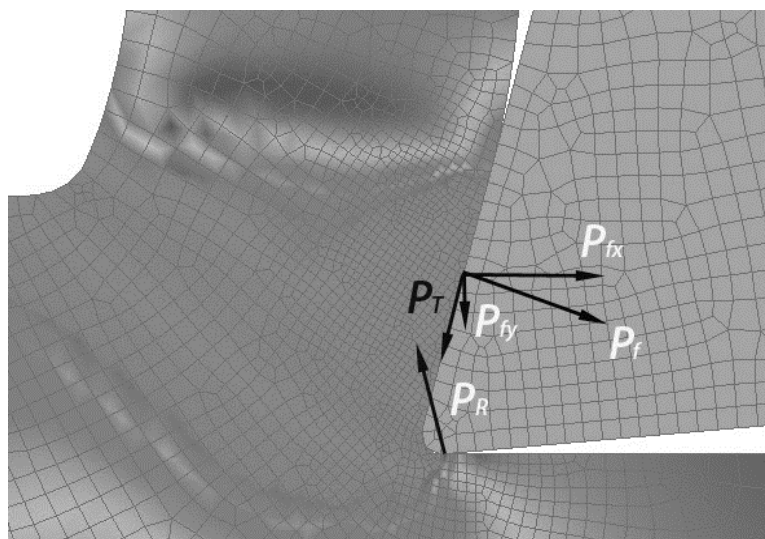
Схема дії сил на передній поверхні інструмента
